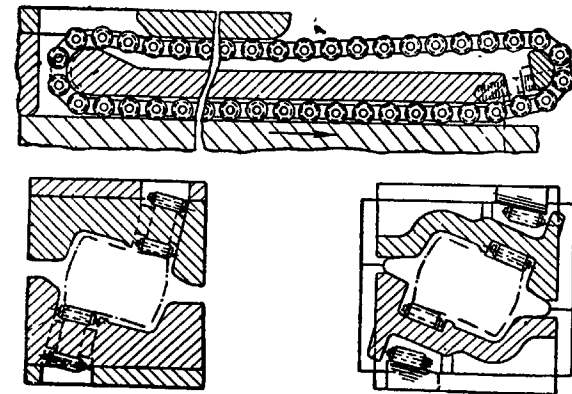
Роликовая проводка непрерывного заготовочного стана
